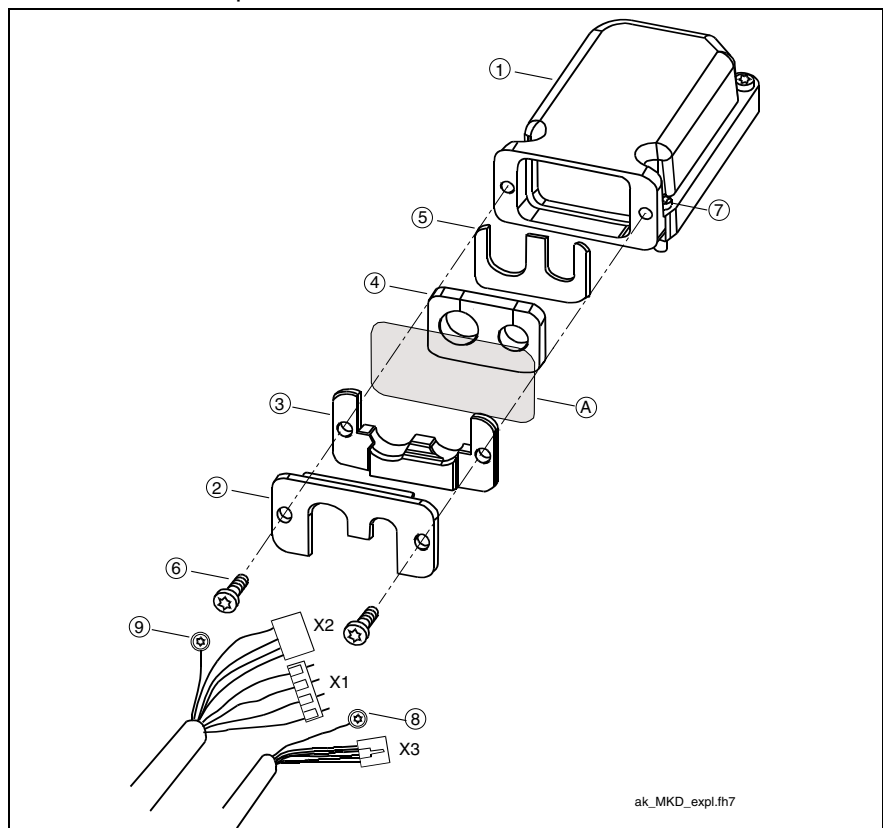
Explosionszeichnung des Anschlußkastens
